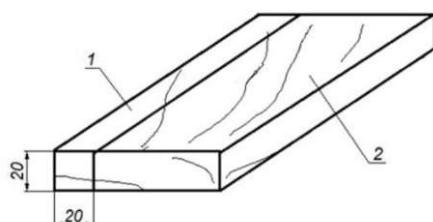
Схема выпиловки заготовки (1) из пластины (2) для изготовления экспериментальных образцов
